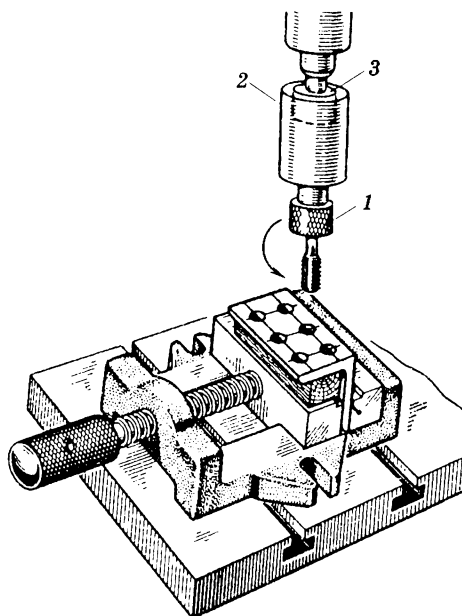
Нарезание внутренней резьбы на сверлильном станке в предохранительном патроне:
